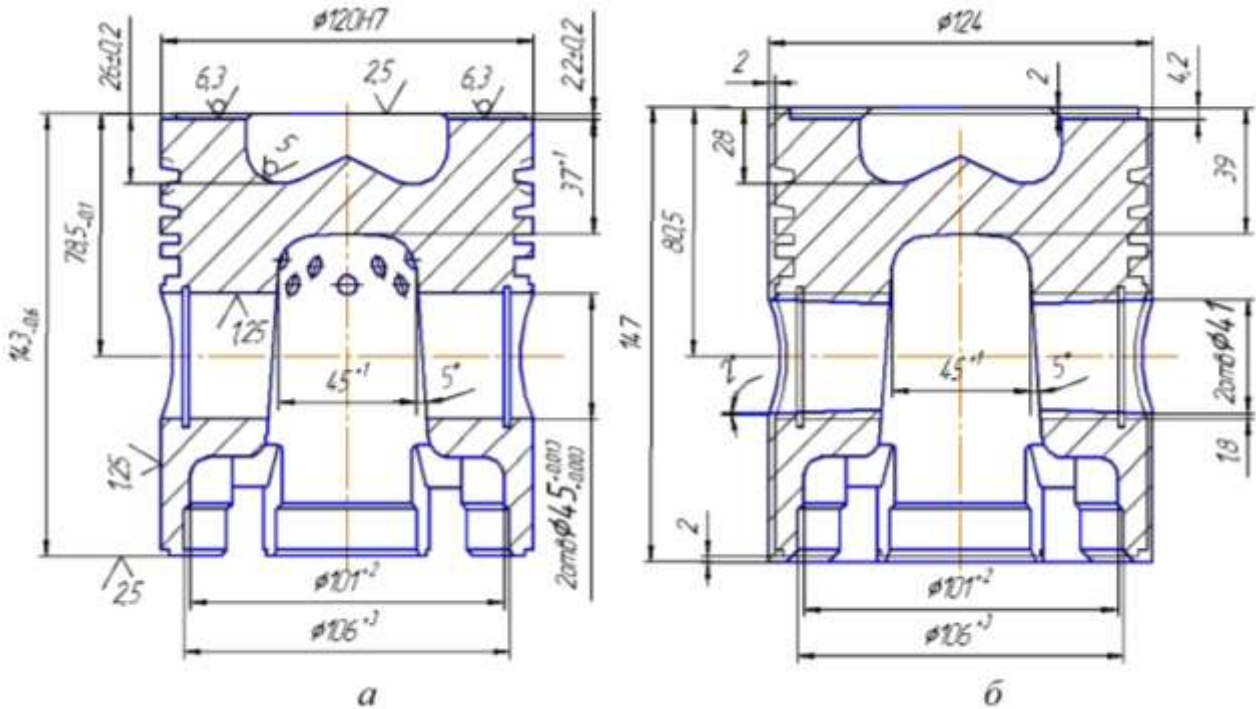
Фрагменти креслення поршня (а) та його виливки (б)
